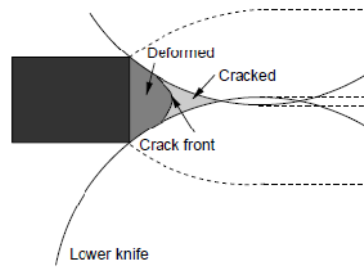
Esquema de la forma de la grieta frontal [2]
